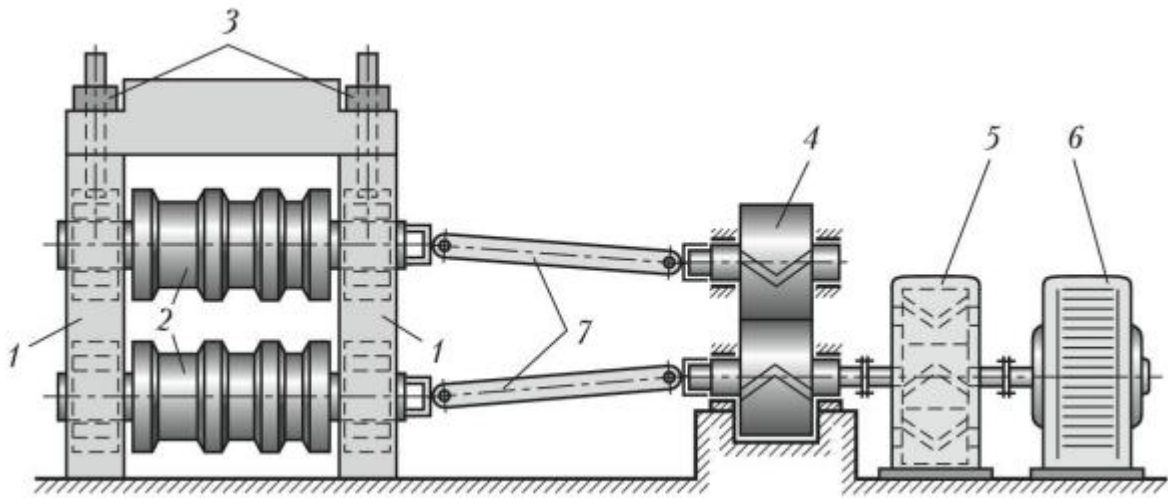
Робоча лінія прокатного стану: 1 – станина, 2 – валки, 3 - натискні механізми, 4 - шестеренна кліть, 5 – редуктор, 6 – електродвигун, 7 - шпинделі
